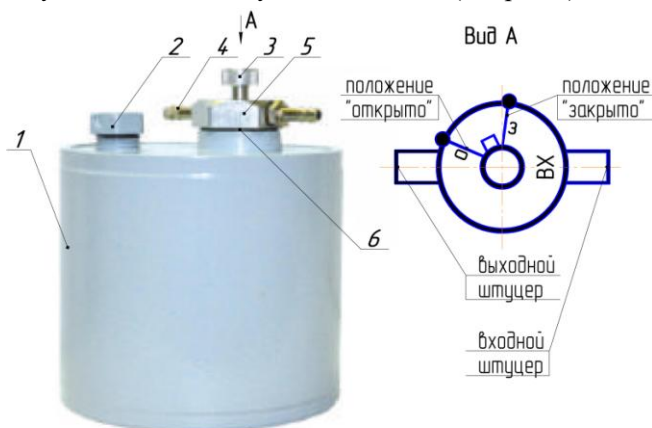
1-корпус; 2-заливная горловина; 3-ручка регулятора;
